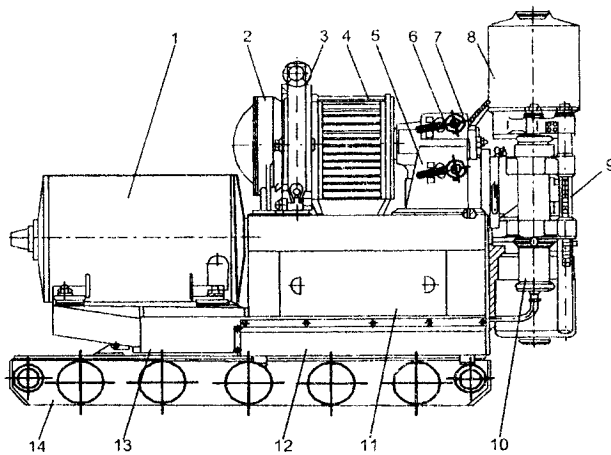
Буровий верстат СКБ-7: 1 – електродвигун постійного струму; 2 – планетарний редуктор лебідки; 3 – гальмо; 4 – лебідка; 5, 6 – рукоятки включення лебідки та обертача; 7 – роздавальна коробка; 8 – патрон; 9 – обертач; 10 – гідроциліндр обертача; 11 – станина; 12 – гідроциліндр переміщення верстата; 13 – кронштейн з площадкою; 14 – рама
